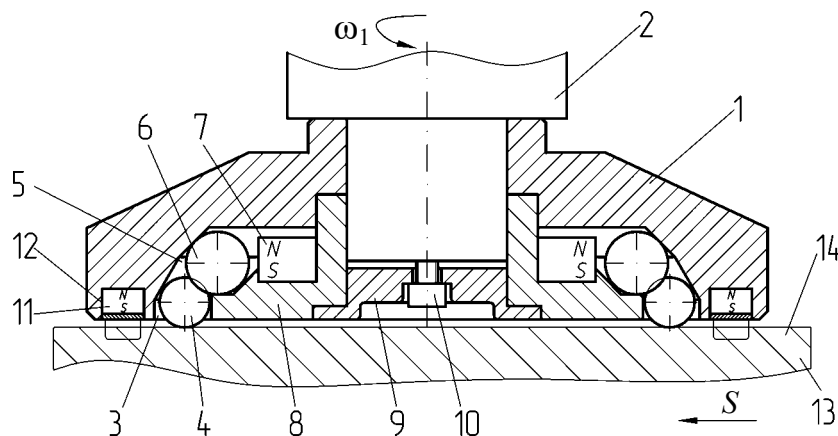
Инструмент для КМДН плоских поверхностей ферромагнитных деталей
